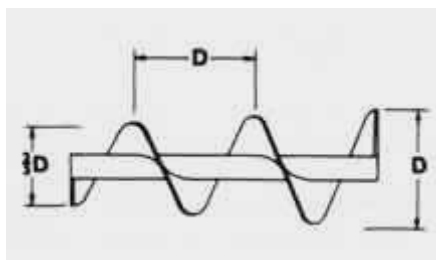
Tornillo de transporte cónico. Fuente: <http://www.kwsmfg.com/services/screw-conveyor-engineering-guide/conveyor-flight-pitch-types.htm>
